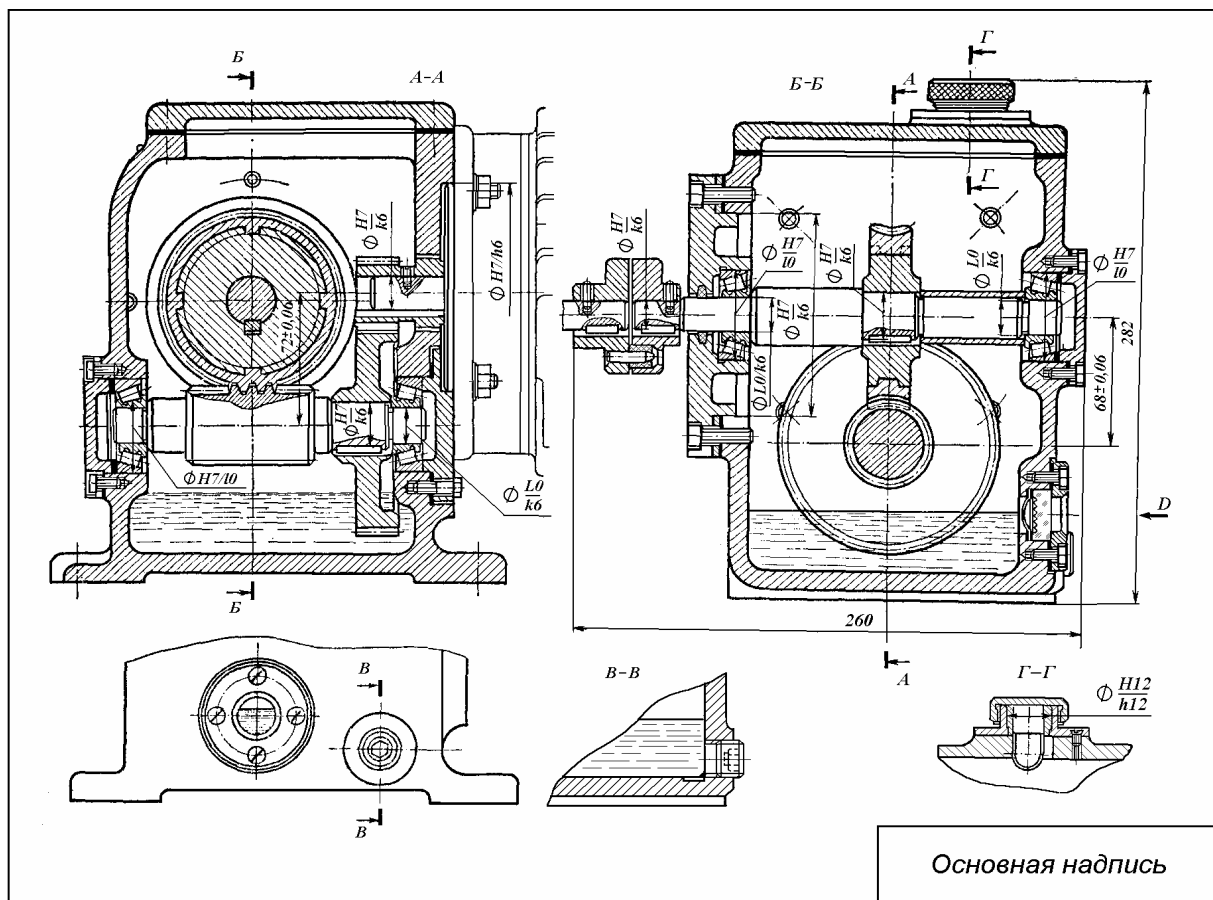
Редуктор цилиндрическо-червячный (лист 1 и 2)
